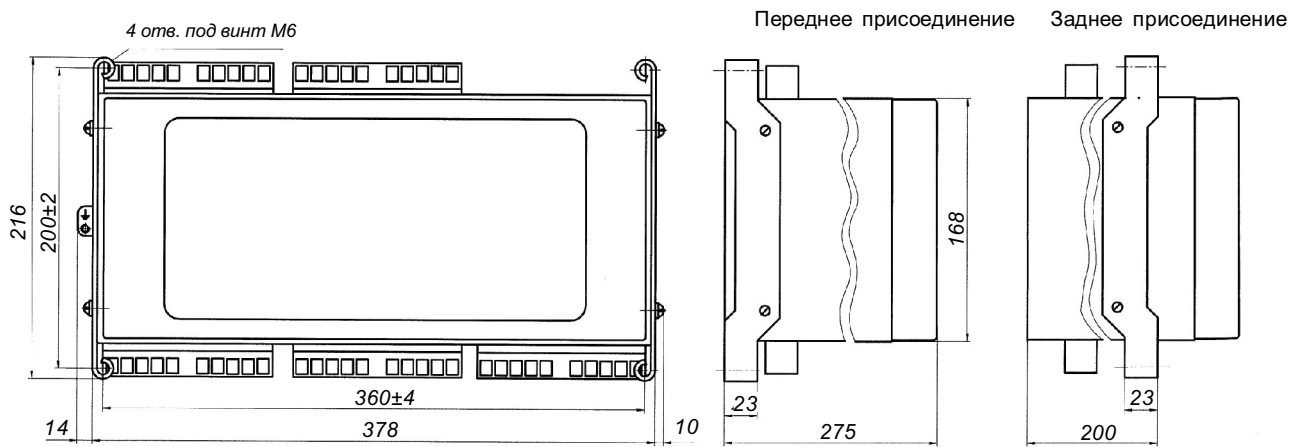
Габаритные, установочные размеры блока типа БЭ 2603
